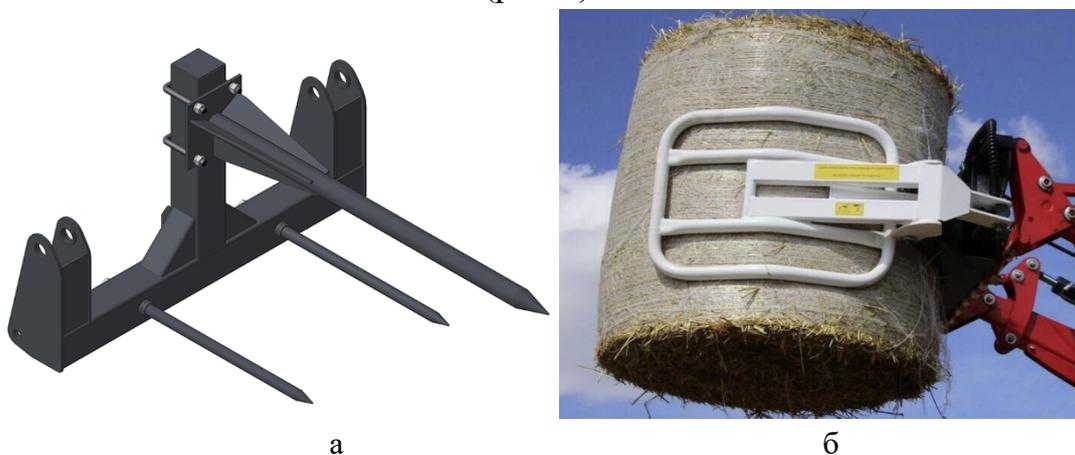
Виды грузозахватных устройств для рулонов прессованных кормов: а - захват для рулонов проникающего типа, б – захват для рулонов обхватывающего типа
